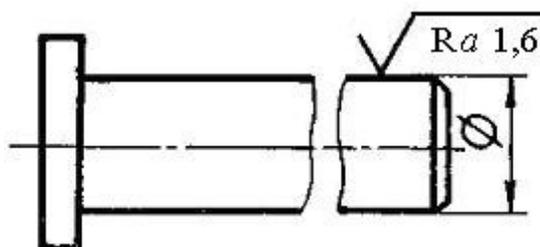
Обозначение шероховатости поверхности на изображении детали с разрывом
